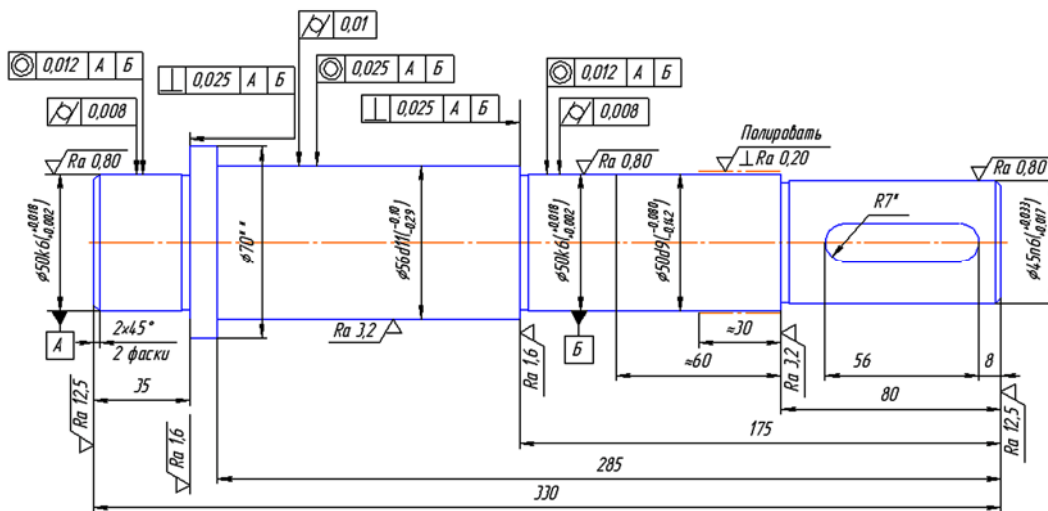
Чертёж вала с указанными допусками
